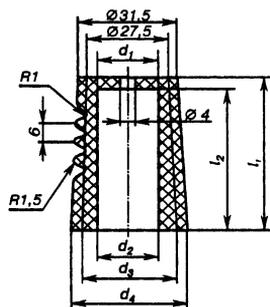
Колпачок полиэтиленовый для изоляторов 6–20 кВ
